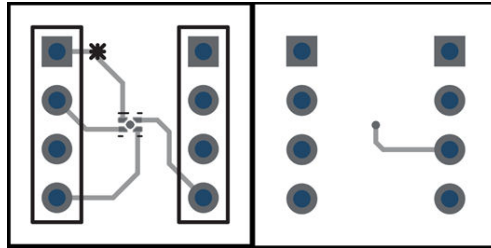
DPW 封装顶层 (左) 和底层 (右) 的 PCB 布局
